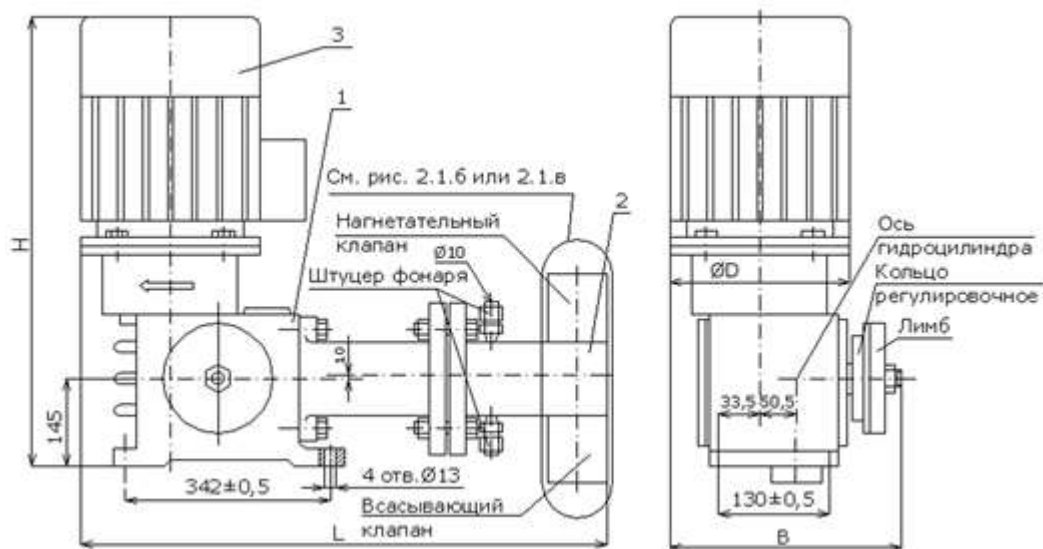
Дозирующий насос с редуктором AP31 с гидроцилиндром двухстороннего действия
